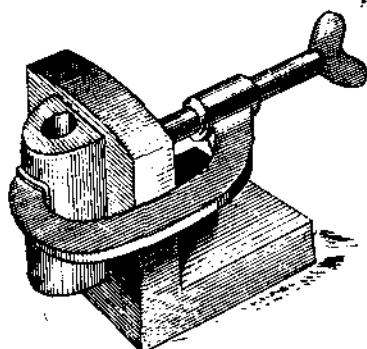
Приспособление для сверления гайки верхней части суппорта.
